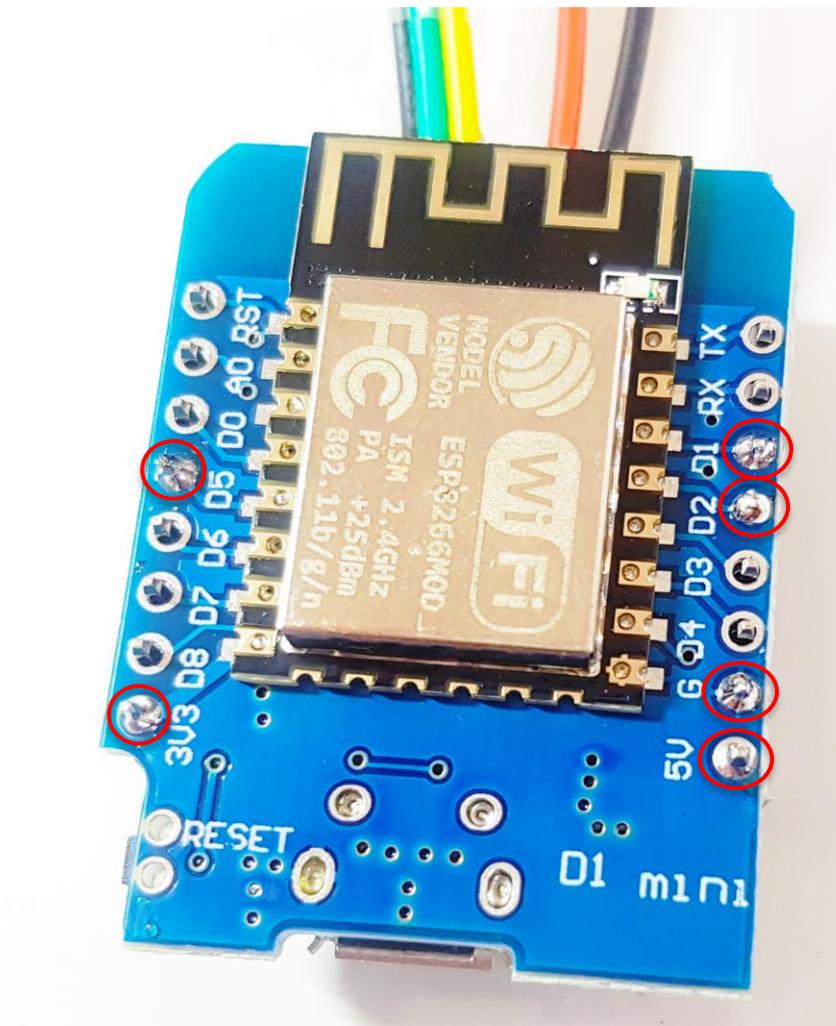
Les 6 points de soudure à réaliser 5V, G, D2, D1, 3V3 et D5
